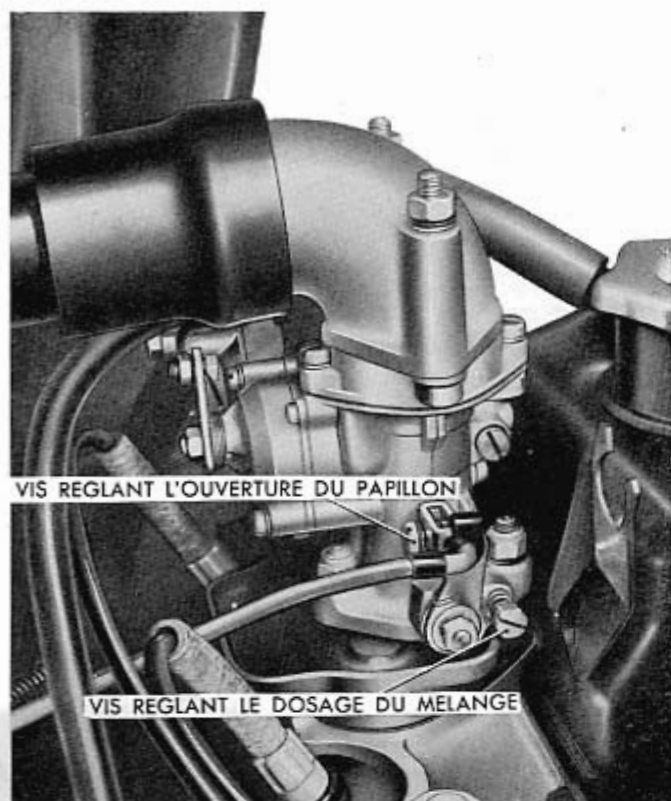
Carburateur Weber 26 IMB 1, monté sur le moteur. Pour le réglage du « ralenti », opérer sur la vis réglant l'ouverture du papillon et sur celle de dosage du mélange.
